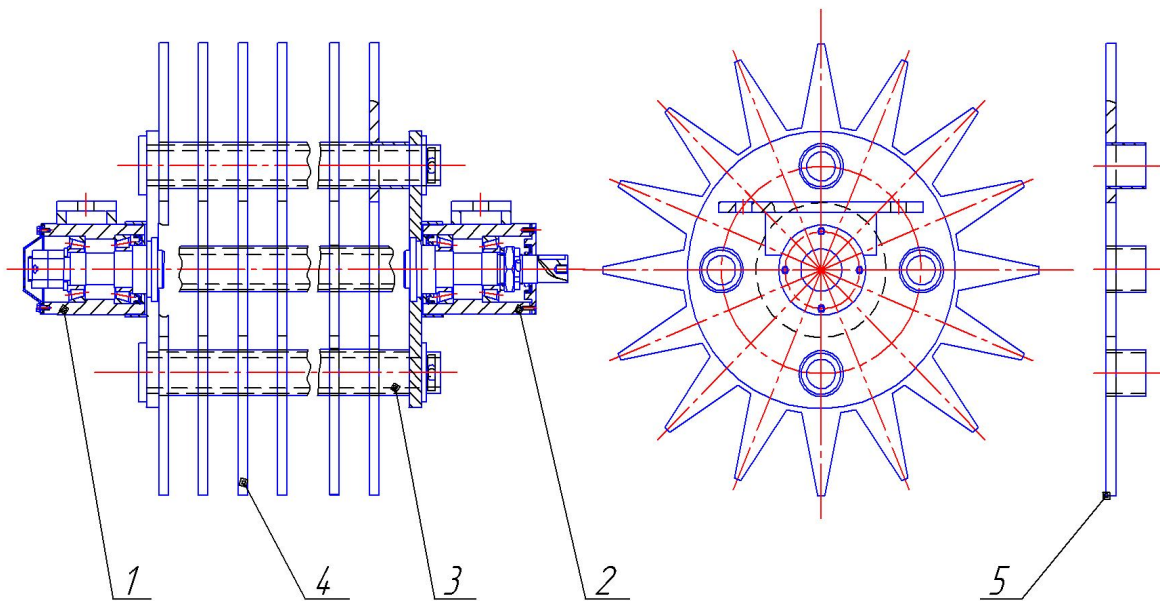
Задний ротор: 1 – опорный узел; 2 – опорно-приводной узел; 3 – дистанционная втулка; 4 – зубчатый диск; 5 – зубчатый диск с приваренными втулками
